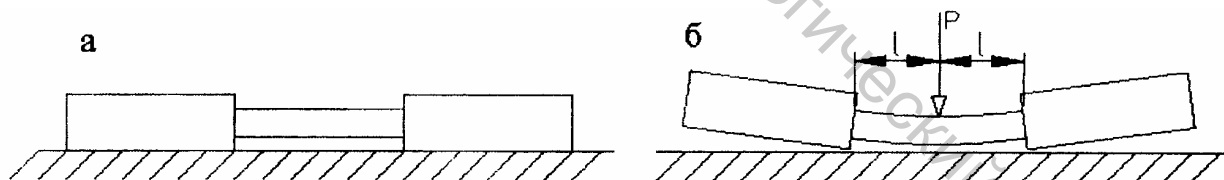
Заготовка до закрепления (а) и в момент после закрепления (б)
